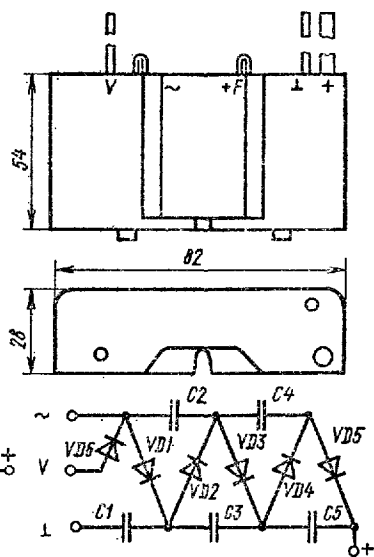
Общий вид, габаритные, присоединительные размеры и электрическая схема умножителя УН 9/27-1,3
